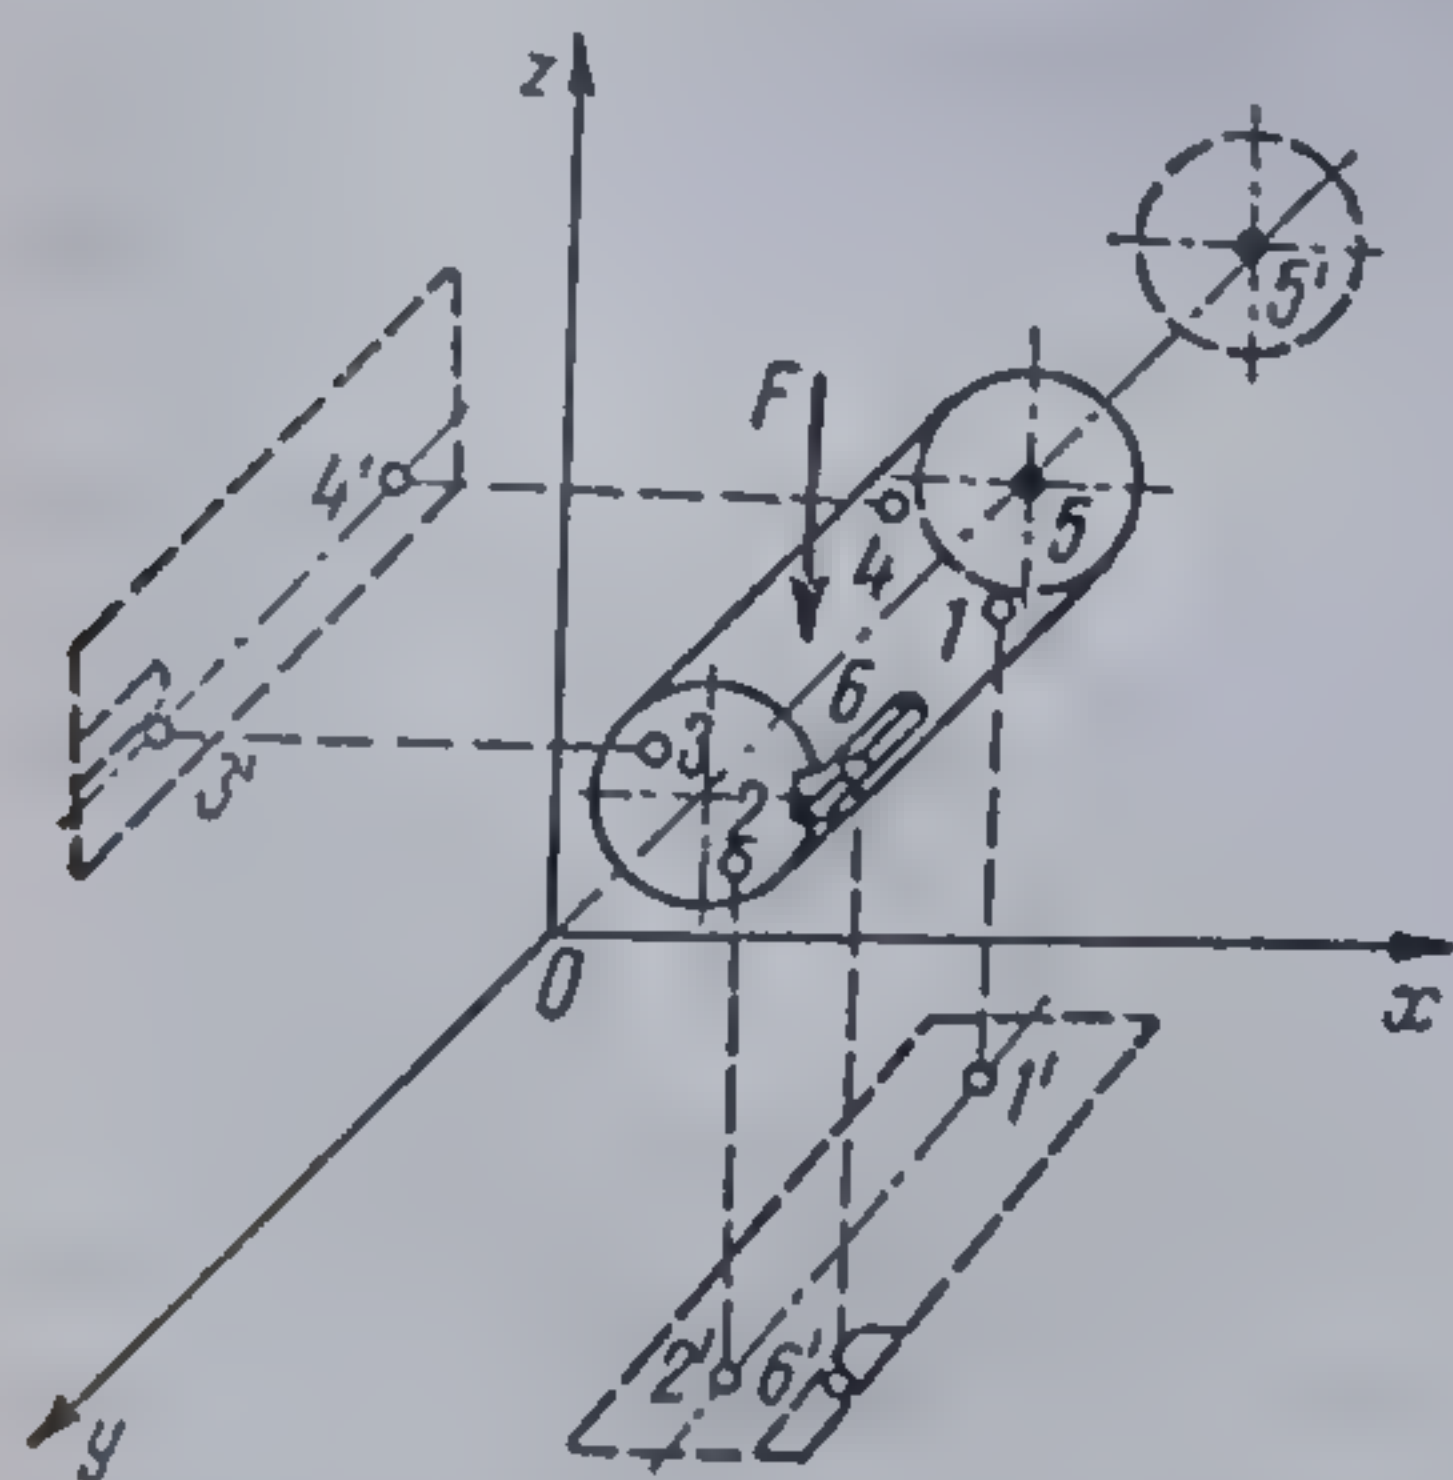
Schema de orientare și fixare în spațiu pentru piese cilindrice lungi.
